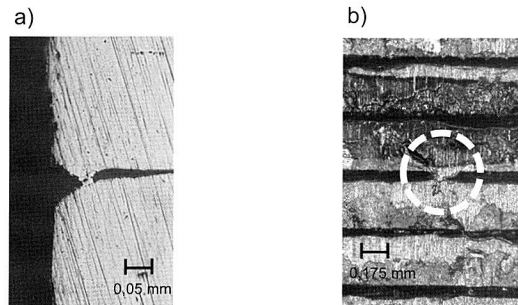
Stanzgratverbindung; a) Schliffbild, b) Oberflächenansicht mit Markierung
